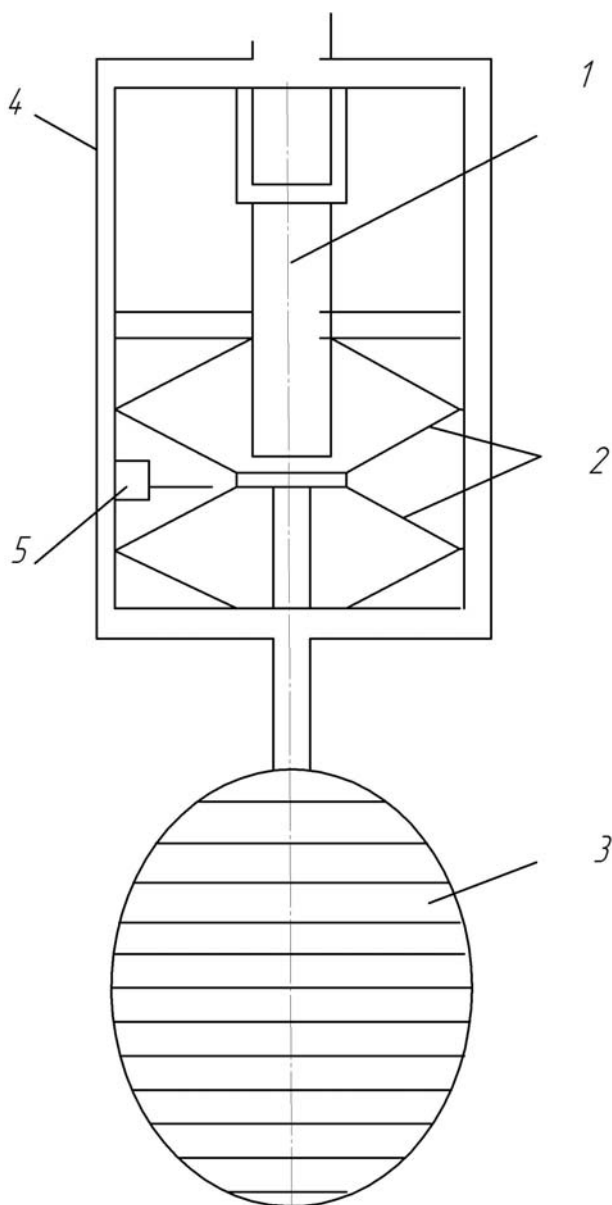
Конструкція вимірювального перетворювача автоматичного шарометру системи ЛТІХПа:
